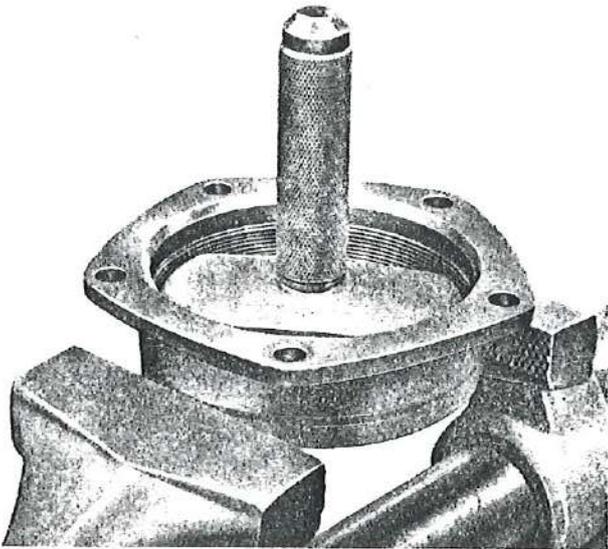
Desmontaje del anillo exterior del rodamiento a rodillos de la caja interna diferencial, mediante el útil A.62027.
